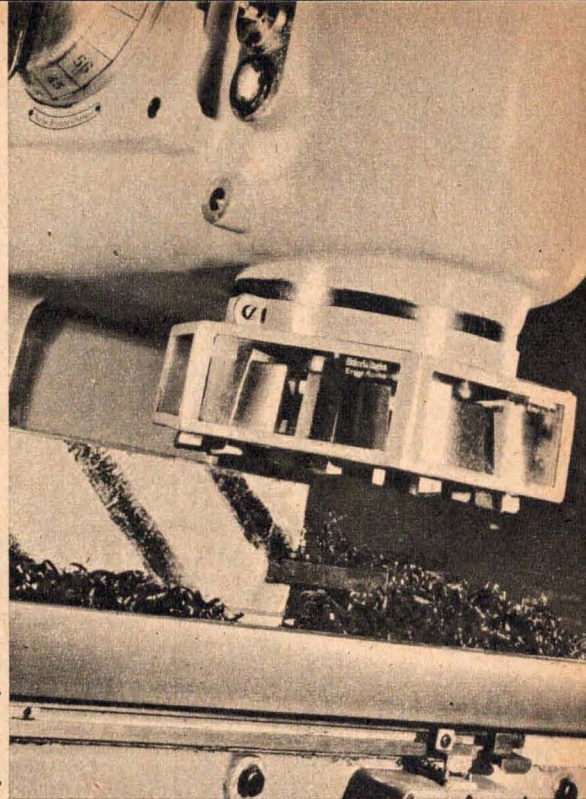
Messerkopf einer Senkrechtfräsmaschine im Einsatz
